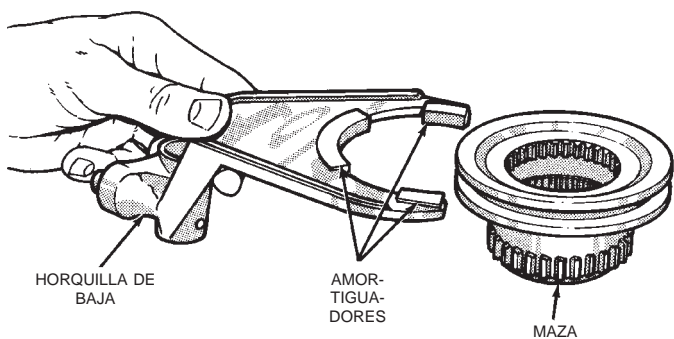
Ensamblaje de la horquilla de baja y la maza
